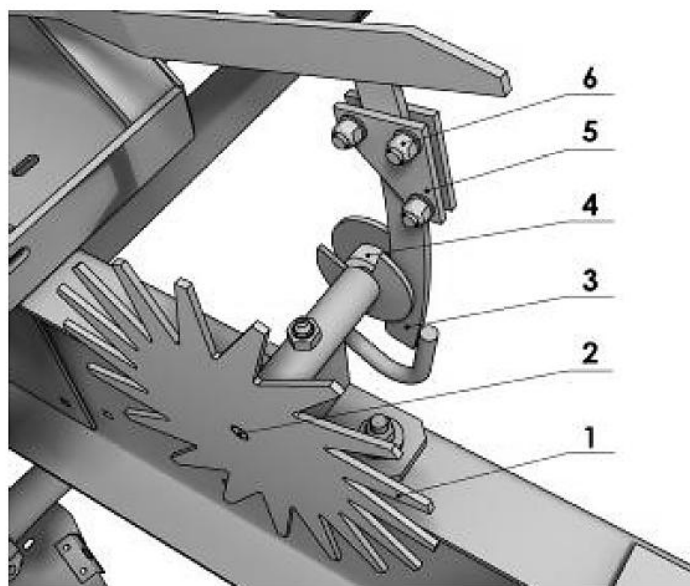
Механизм регулирования длины тюка: 1 – колесо мерительное;
